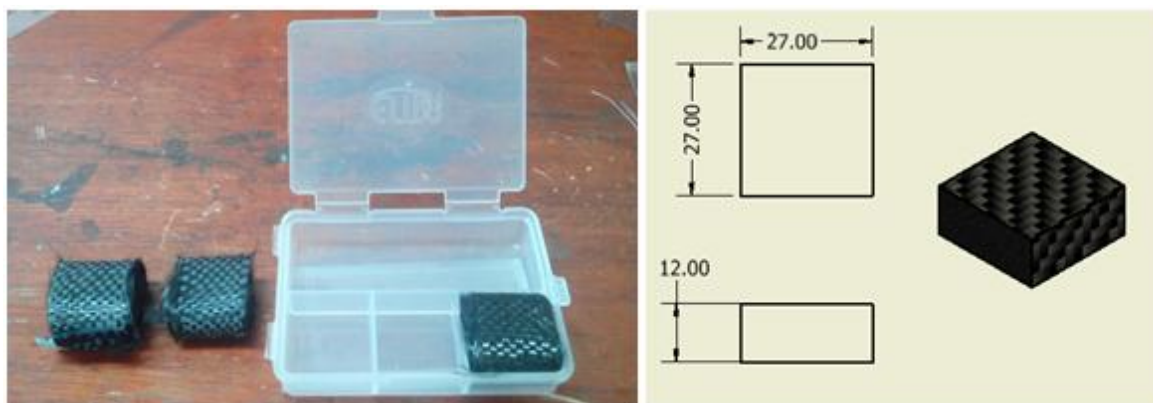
MOLDE Y TELA PARA MOLDEAR PROBETAS DE HEXAGONALES (IZQUIERDA). DIMENSIONES Y APARIENCIA DESPUÉS DEL MOLDEO (DERECHA)
